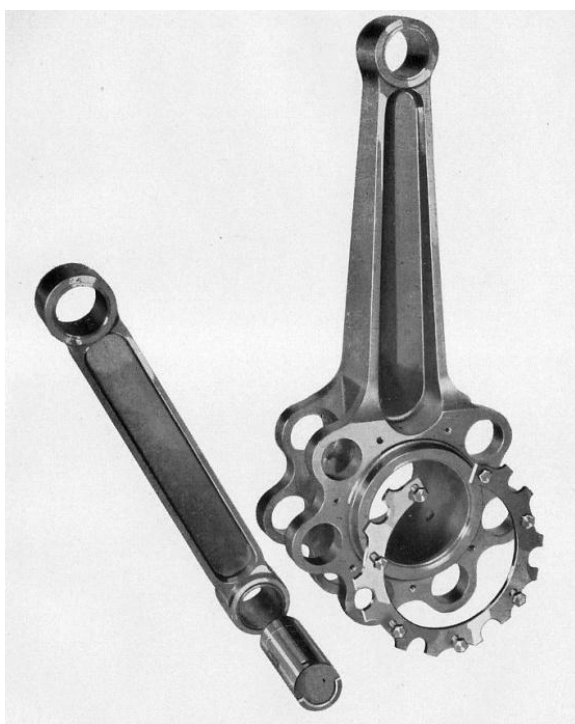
Hlavní ojnice motoru Verner Scarlett 7H [32]
